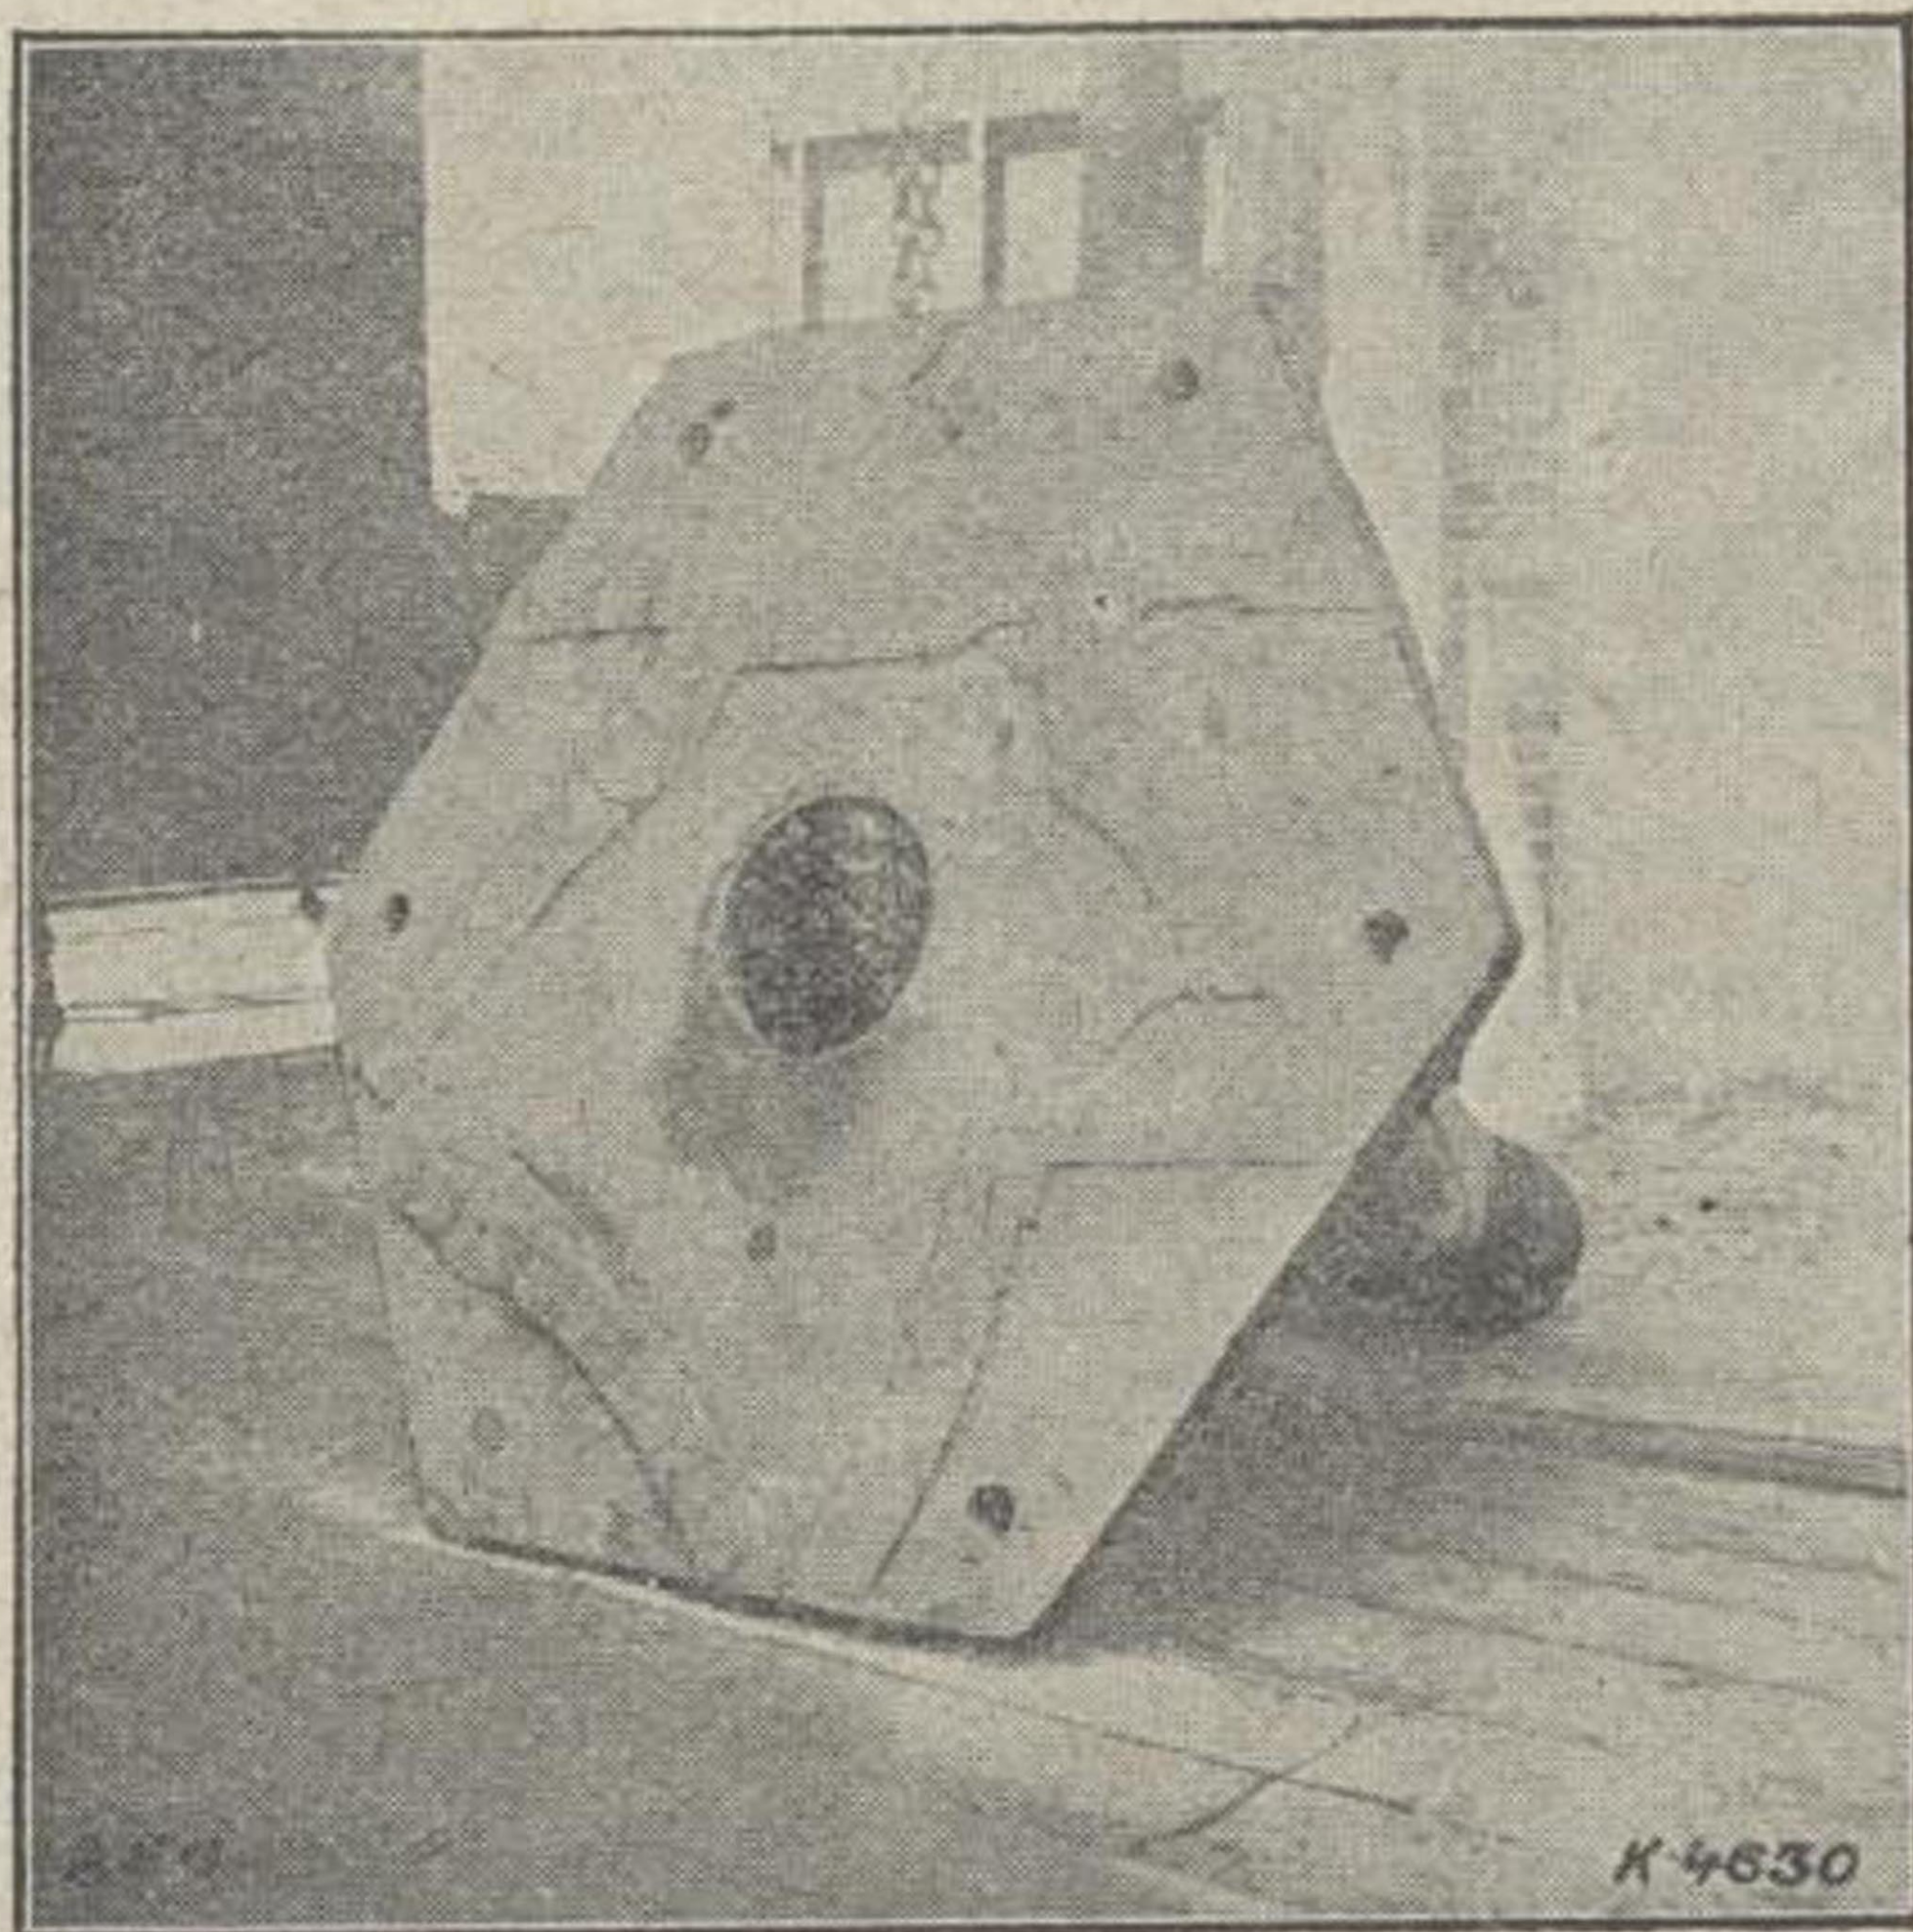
Silla de la fig. 20 reparada con soldadura por arco.
